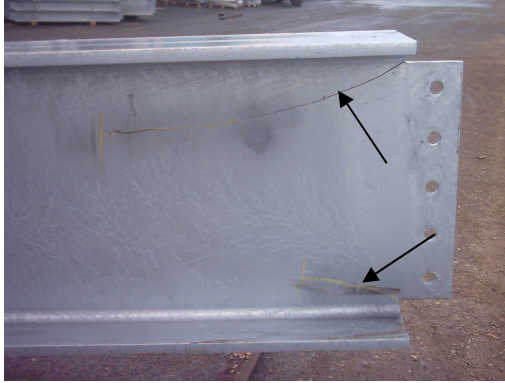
Ejemplo de perfil IPE con fisuras surgidas durante la galvanización.
